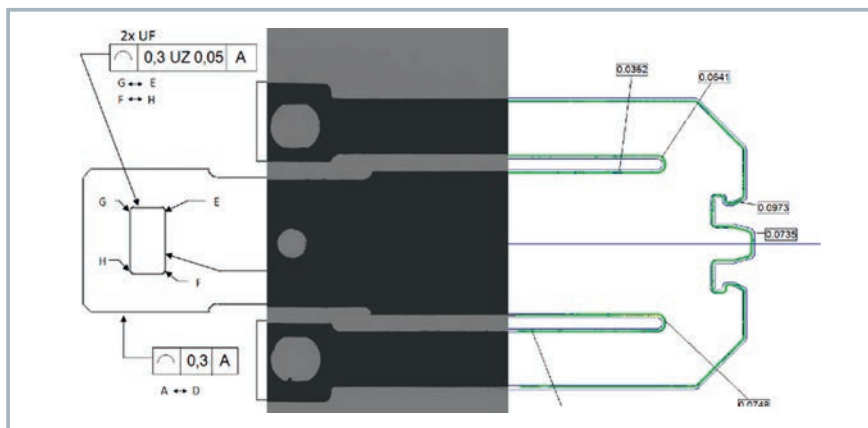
Links: Zeichnung mit Linienprofiltoleranzen, Mitte: automatische Erfassung des gesamten Werkstücks in hoher Auflösung durch Raster-scanning, rechts: Einpassung in die Toleranzzonen mit ToleranceFit (© Werth)
